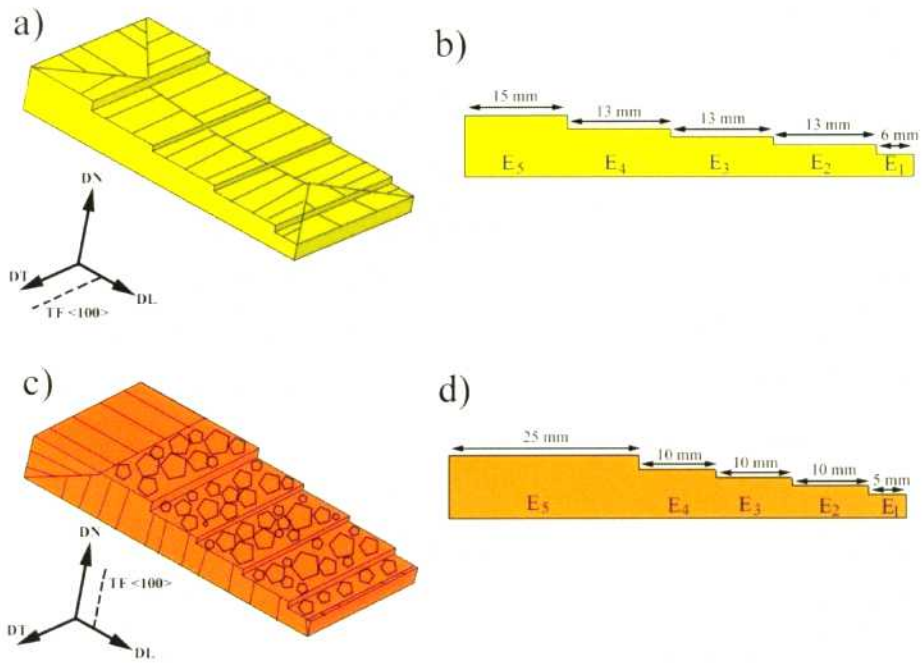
Probetas para laminación. a) Ubicación de las fibras en LAM1, b) sección longitudinal de LAM1, c) ubicación de las fibras LAM2, d) sección longitudinal de LAM2.
